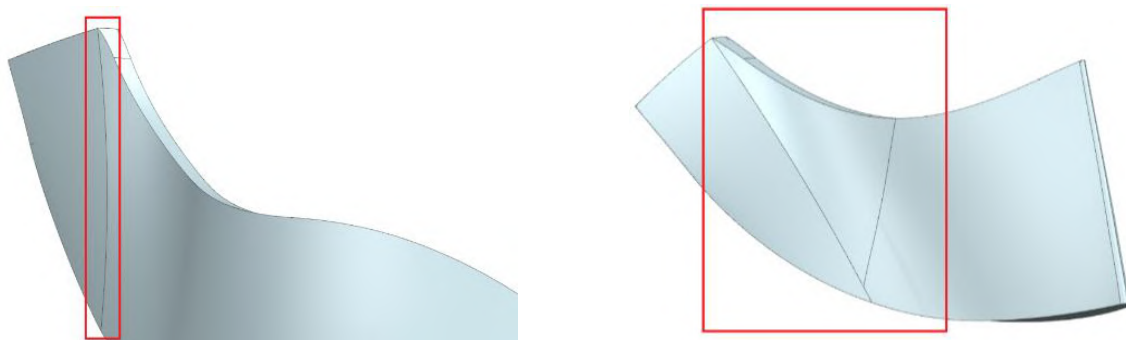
Эскизный чертеж проточной части компрессора с указанием контуров подрезки
